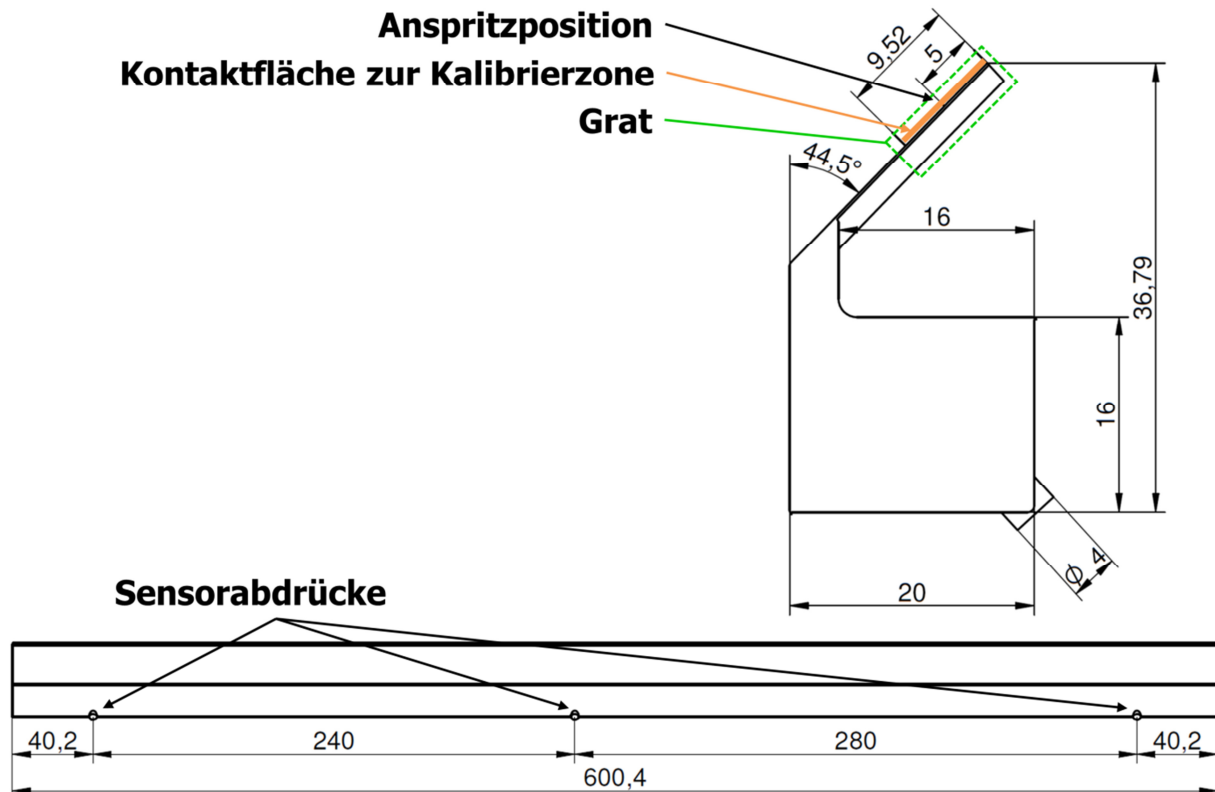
Bauteilabmessungen (in mm); Seitenansicht (unten) und Bauteilquerschnitt (oben).
